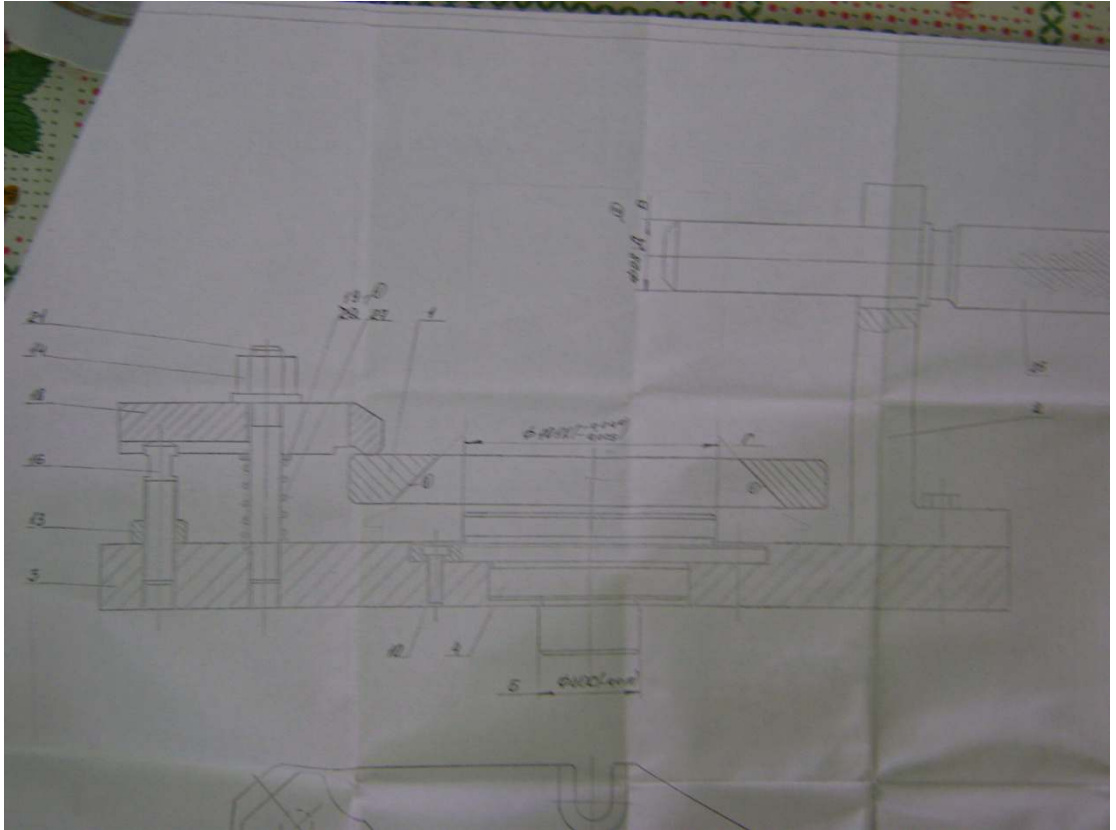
Фрезерное приспособление ВУ7221 – 6335
